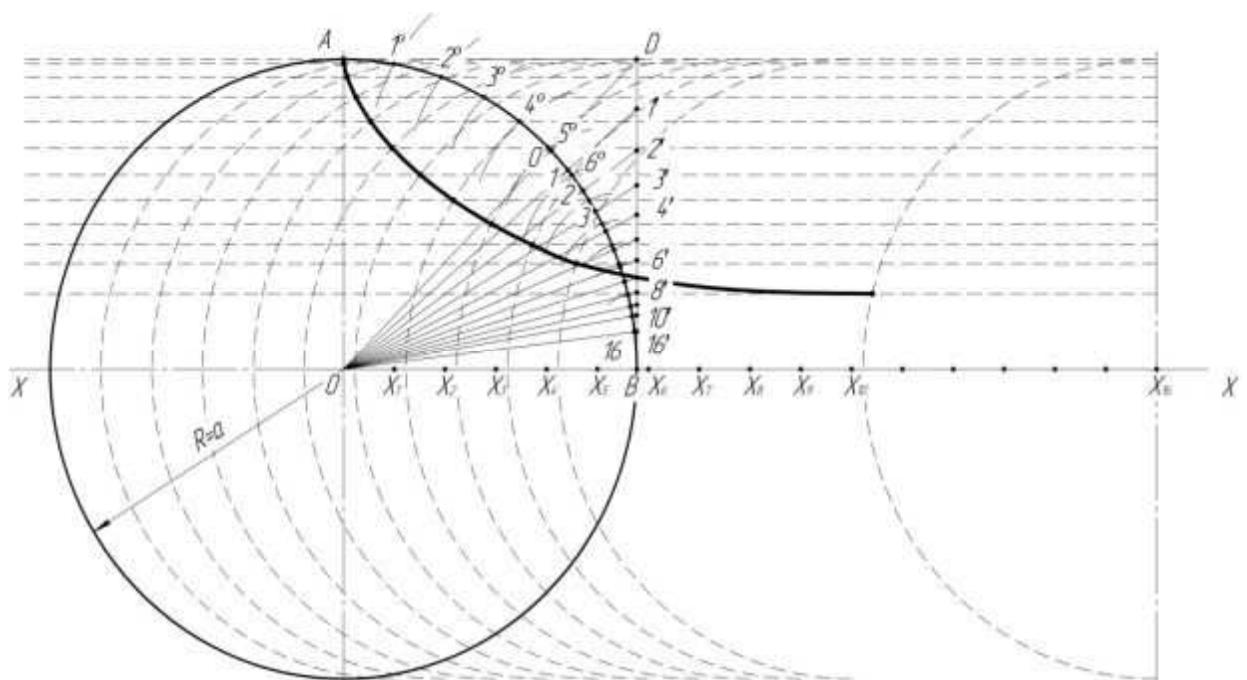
Построение профиля поверхности рабочего канала формированной головки пресса
